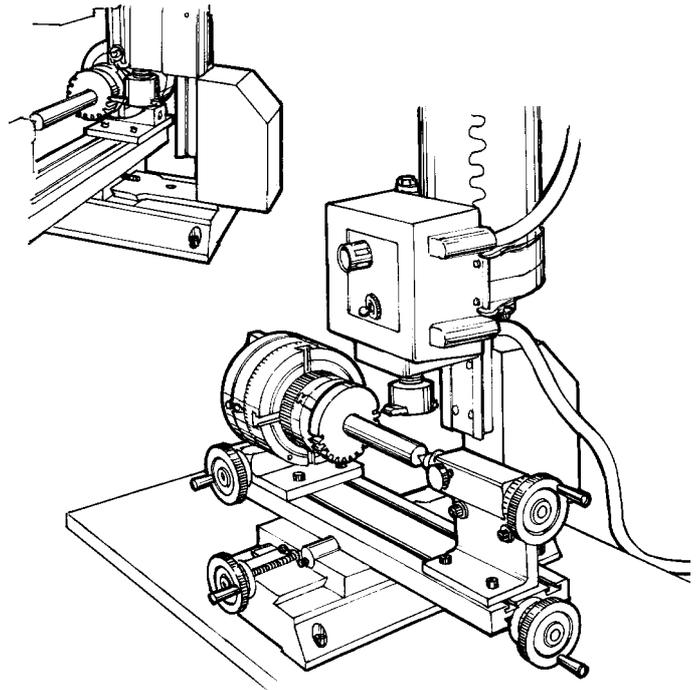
Aufbau einer Zahnradfräse. Die kleine Zeichnung zeigt den Aufbau der Frässäule um größere Durchmesser bearbeiten zu können
